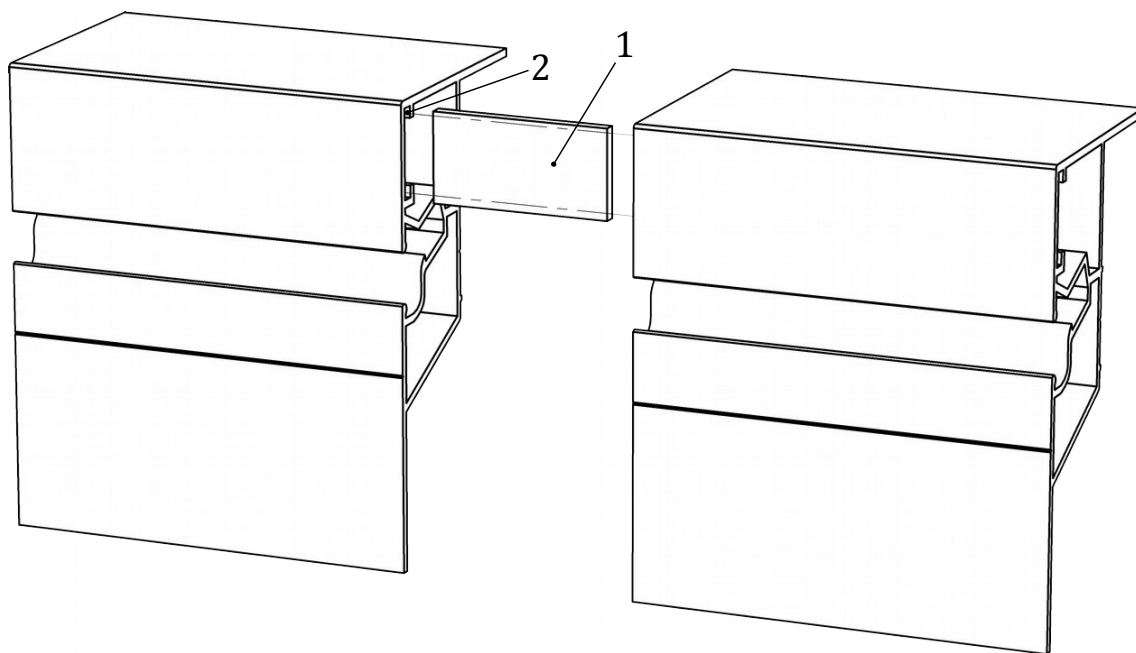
Стыковка профилей КП при помощи соединительной пластины
